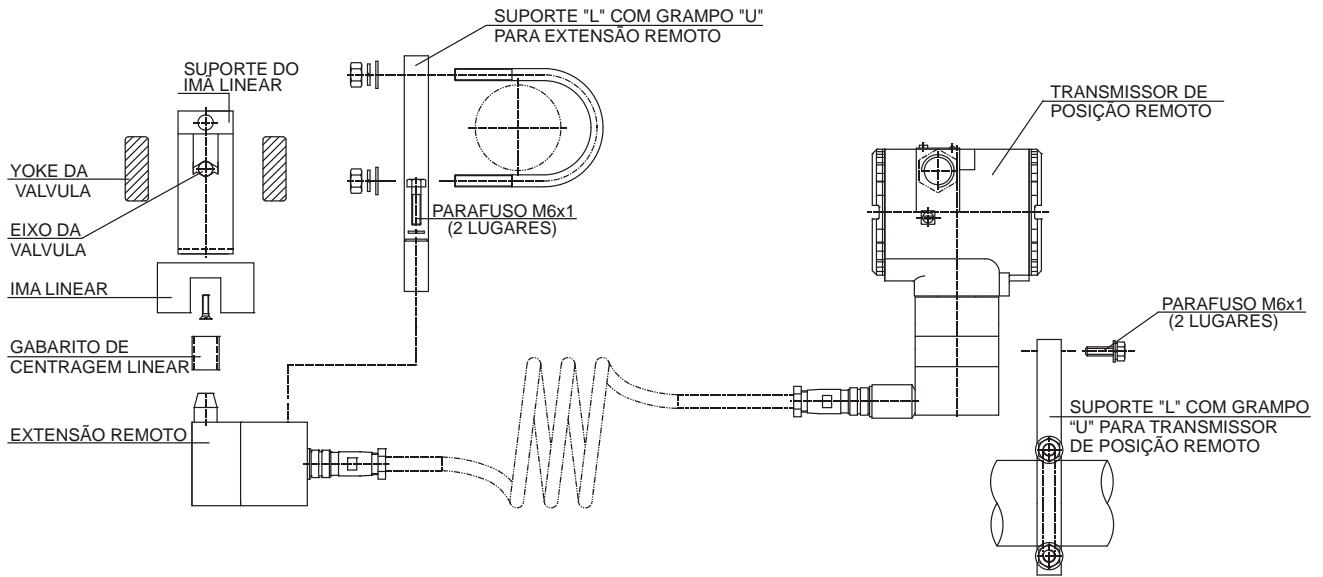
Transmissor de Posição em Atuador Linear com sensor de Posição Remoto
